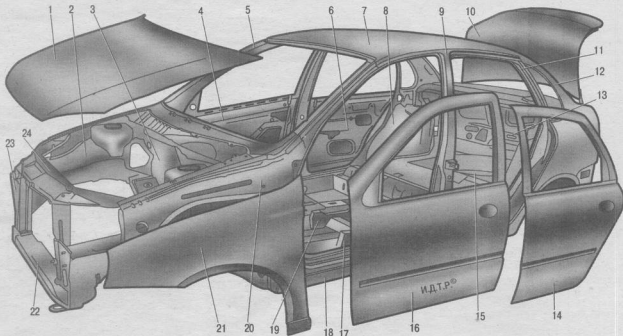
Детали каркаса кузова автомобиля ВАЗ-1118: 1 — капот; 2 — правый передний лонжерон; 3 — щиток передка; 4 — правая передняя дверь; 5 — стойка ветрового окна; 6 — правая задняя дверь; 7 — панель крыши; 8 — арка заднего колеса с опорой пружины задней подвески; 9 — центральная стойка; 10 — крышка багажника; 11 — задняя стойка; 12 — рамка окна боковины; 13 — панель задка; 14 — левая задняя дверь; 15 — ниша запасного колеса; 16 — левая передняя дверь; 17 — кронштейн крепления переднего сиденья; 18 — панель боковины; 19 — поперечина пола; 20 — брызговики левого переднего крыла; 21 — левое переднее крыло; 22 — нижняя поперечина рамки радиатора; 23 — стойка рамки радиатора; 24 — верхняя поперечина рамки радиатора
